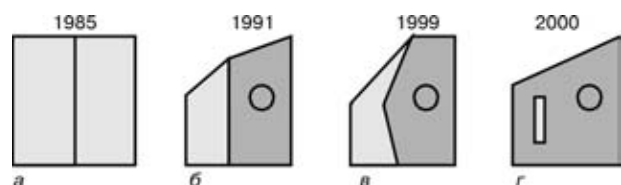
Этапы развития конструкций ССЗ-ТВ: а — укрупненный формат; б — с прямолинейным сварным швом; в — с нелинейным сварным швом; г — со вставным элементом
